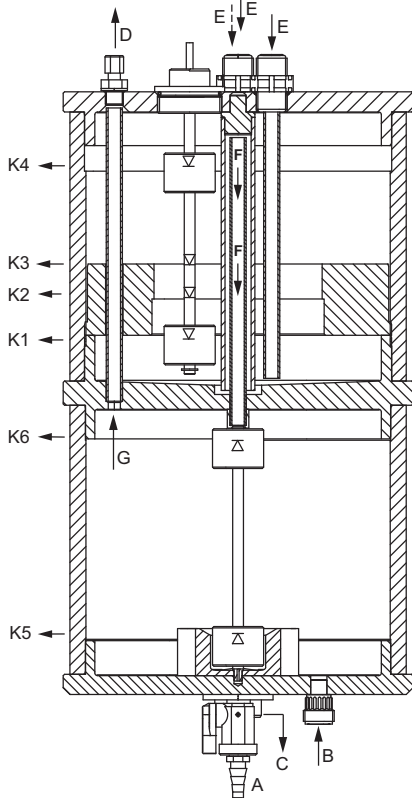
Реактор и внутренний дозирочный резервуар (OCD-162-5/-10/-30)
